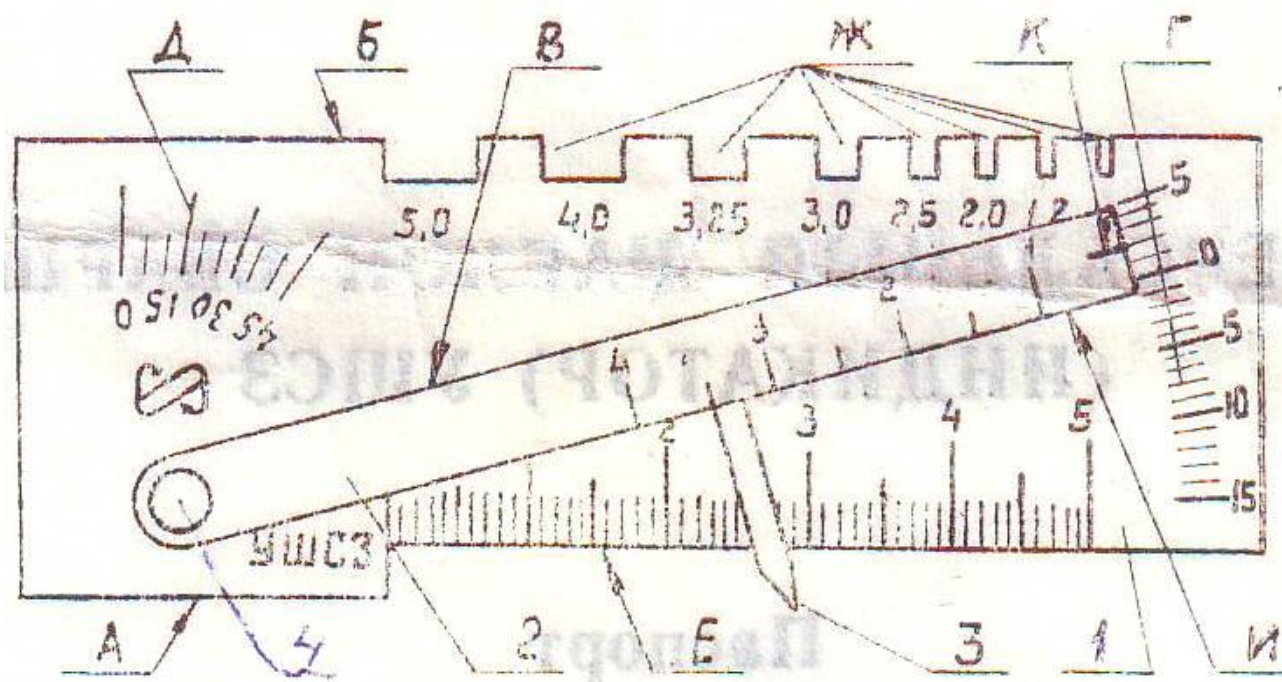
Универсальный шаблон сварщика УШСЗ
